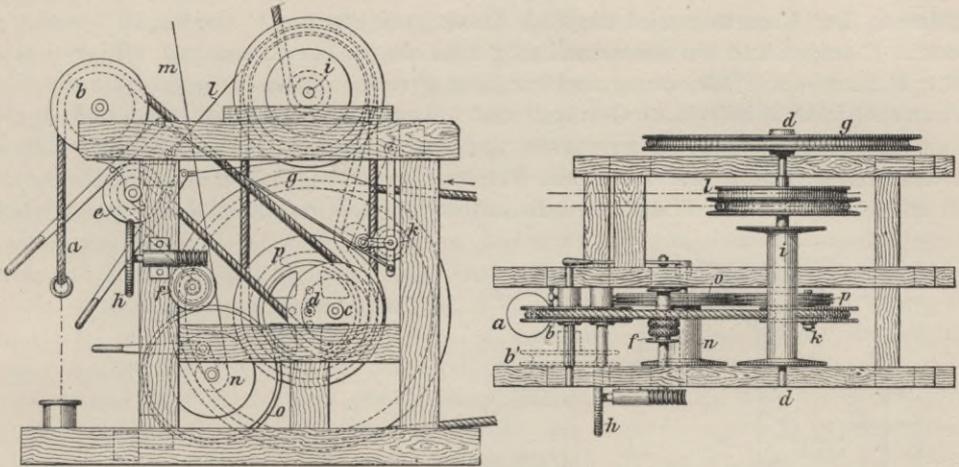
Bohrwinde von Fauck. M. 1 : 50. 1896.
